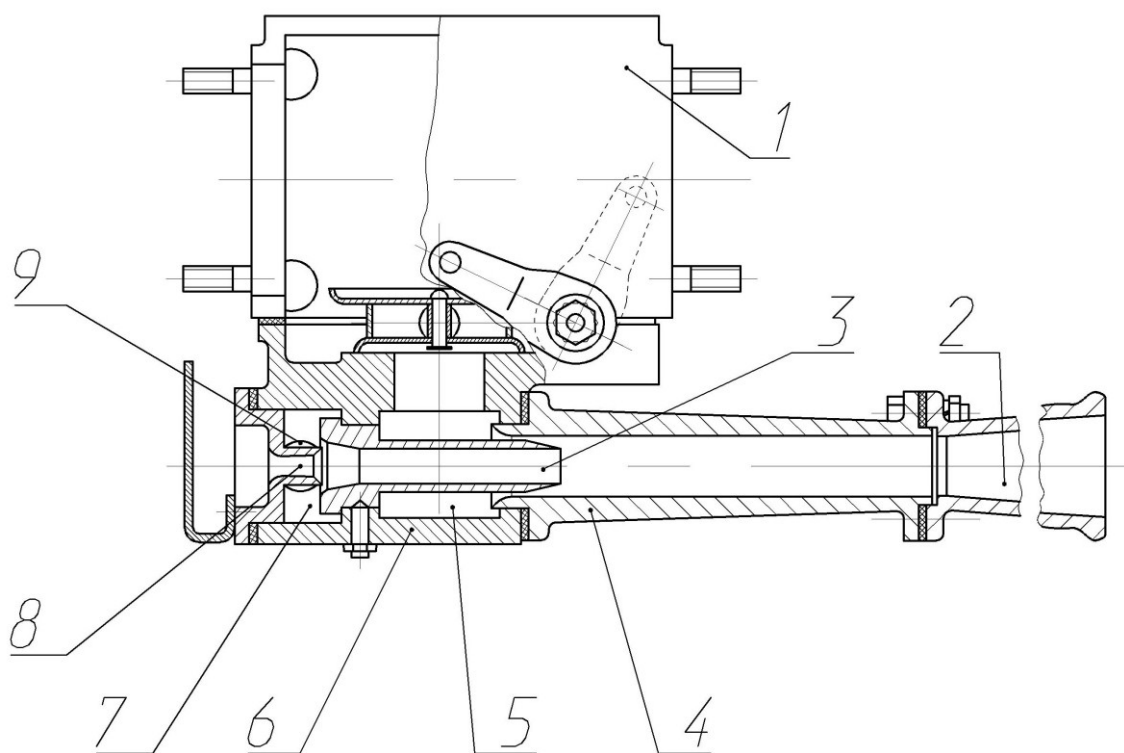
Двухступенчатый вакуумный насос для пожарных аварийно-спасательных автомобилей с дизельным двигателем: 1- корпус распределительной камеры; 2 – диффузор; 3 - промежуточное сопло; 4 - приемное сопло; 5 - промежуточная камера, 6 - корпус, 7 - камера разрежения; 8 - воздушное сопло; 9 – отверстие для подключения трубопровода вакуумной системы.
